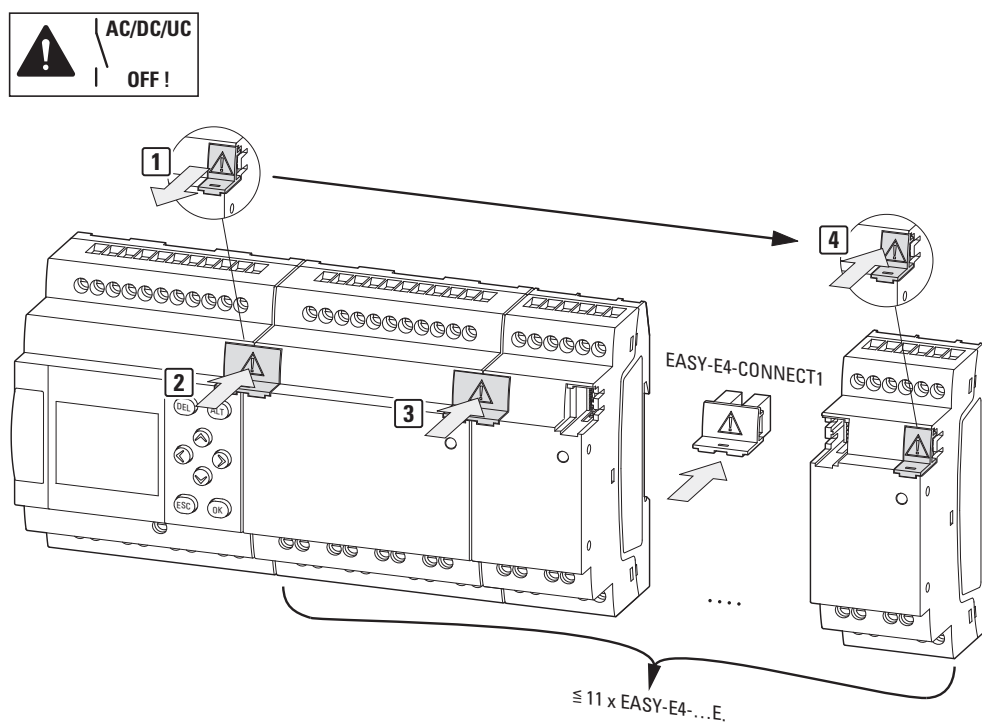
Montaggio dell'apparecchio base con espansioni.
